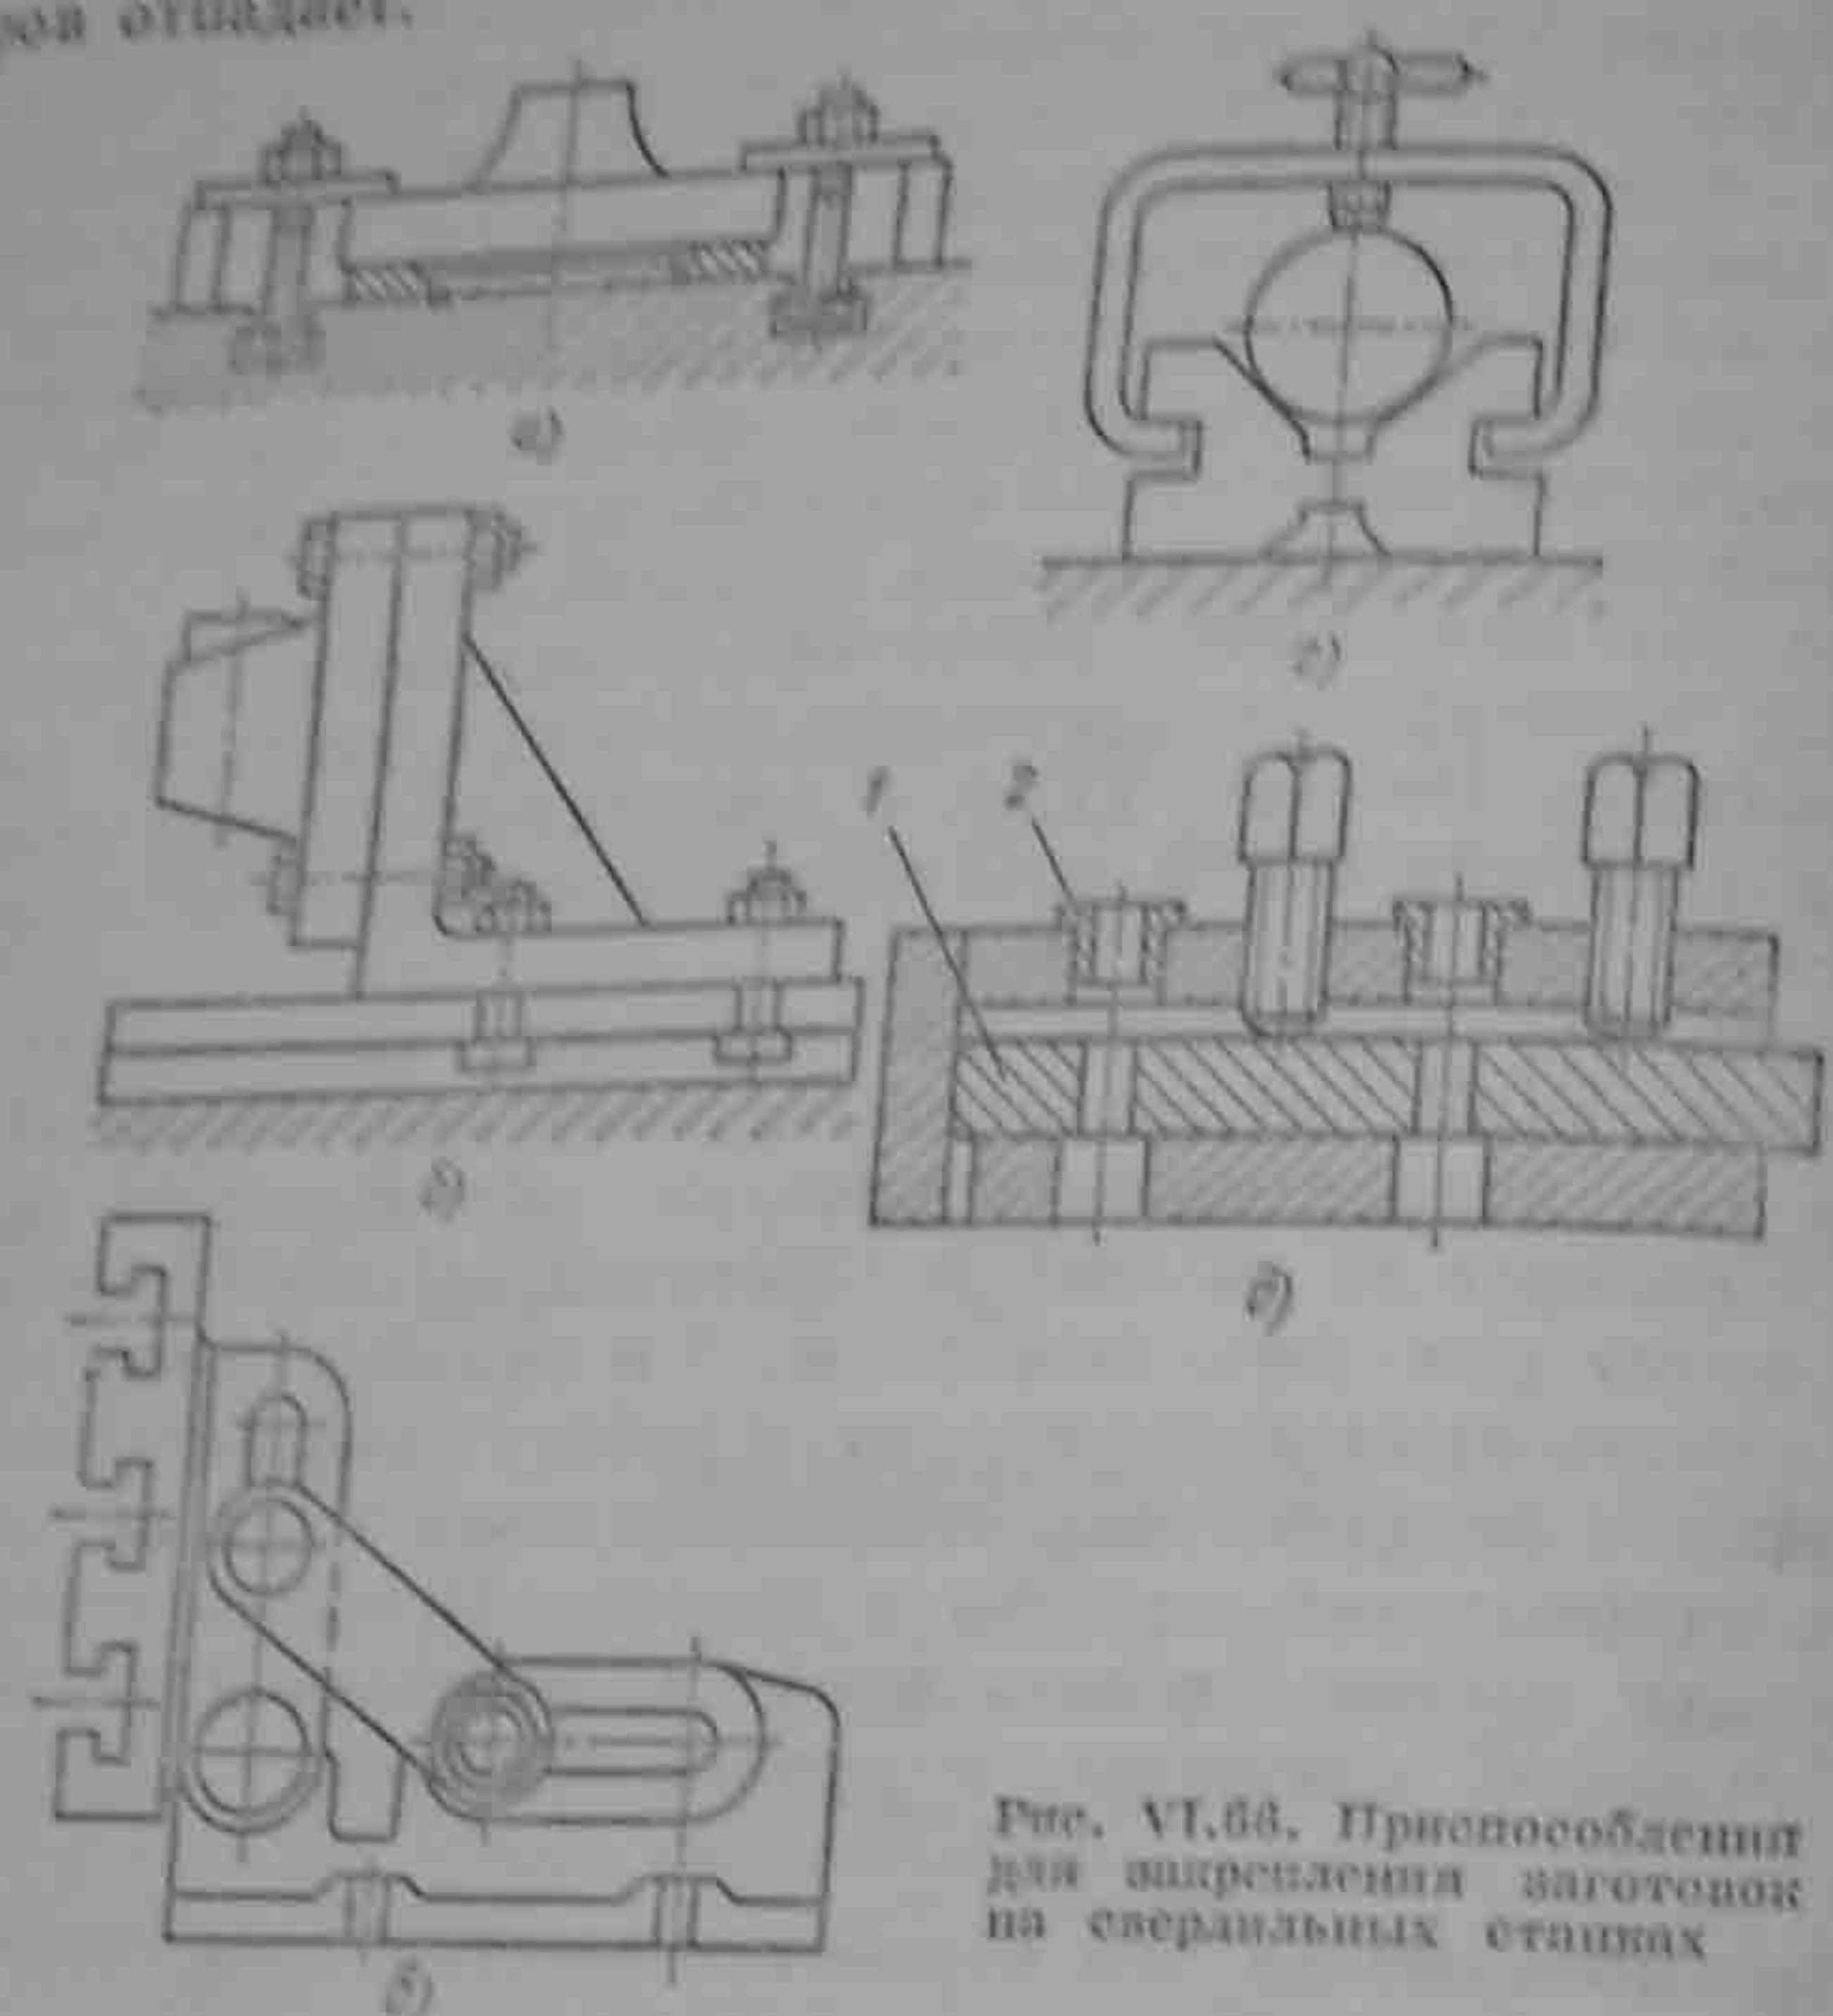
Приспособления для закрепления заготовок на сверлильных станках
